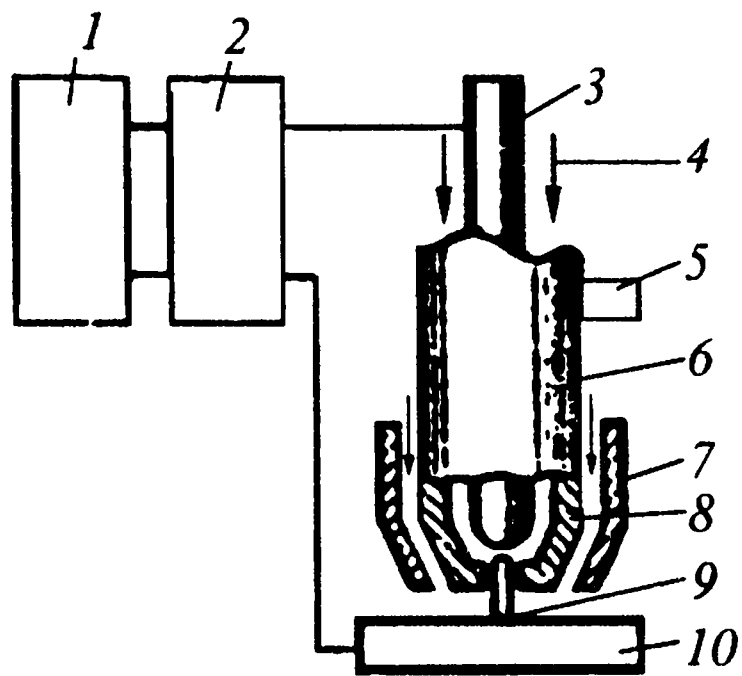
Схема сварки плазменной дугой:
